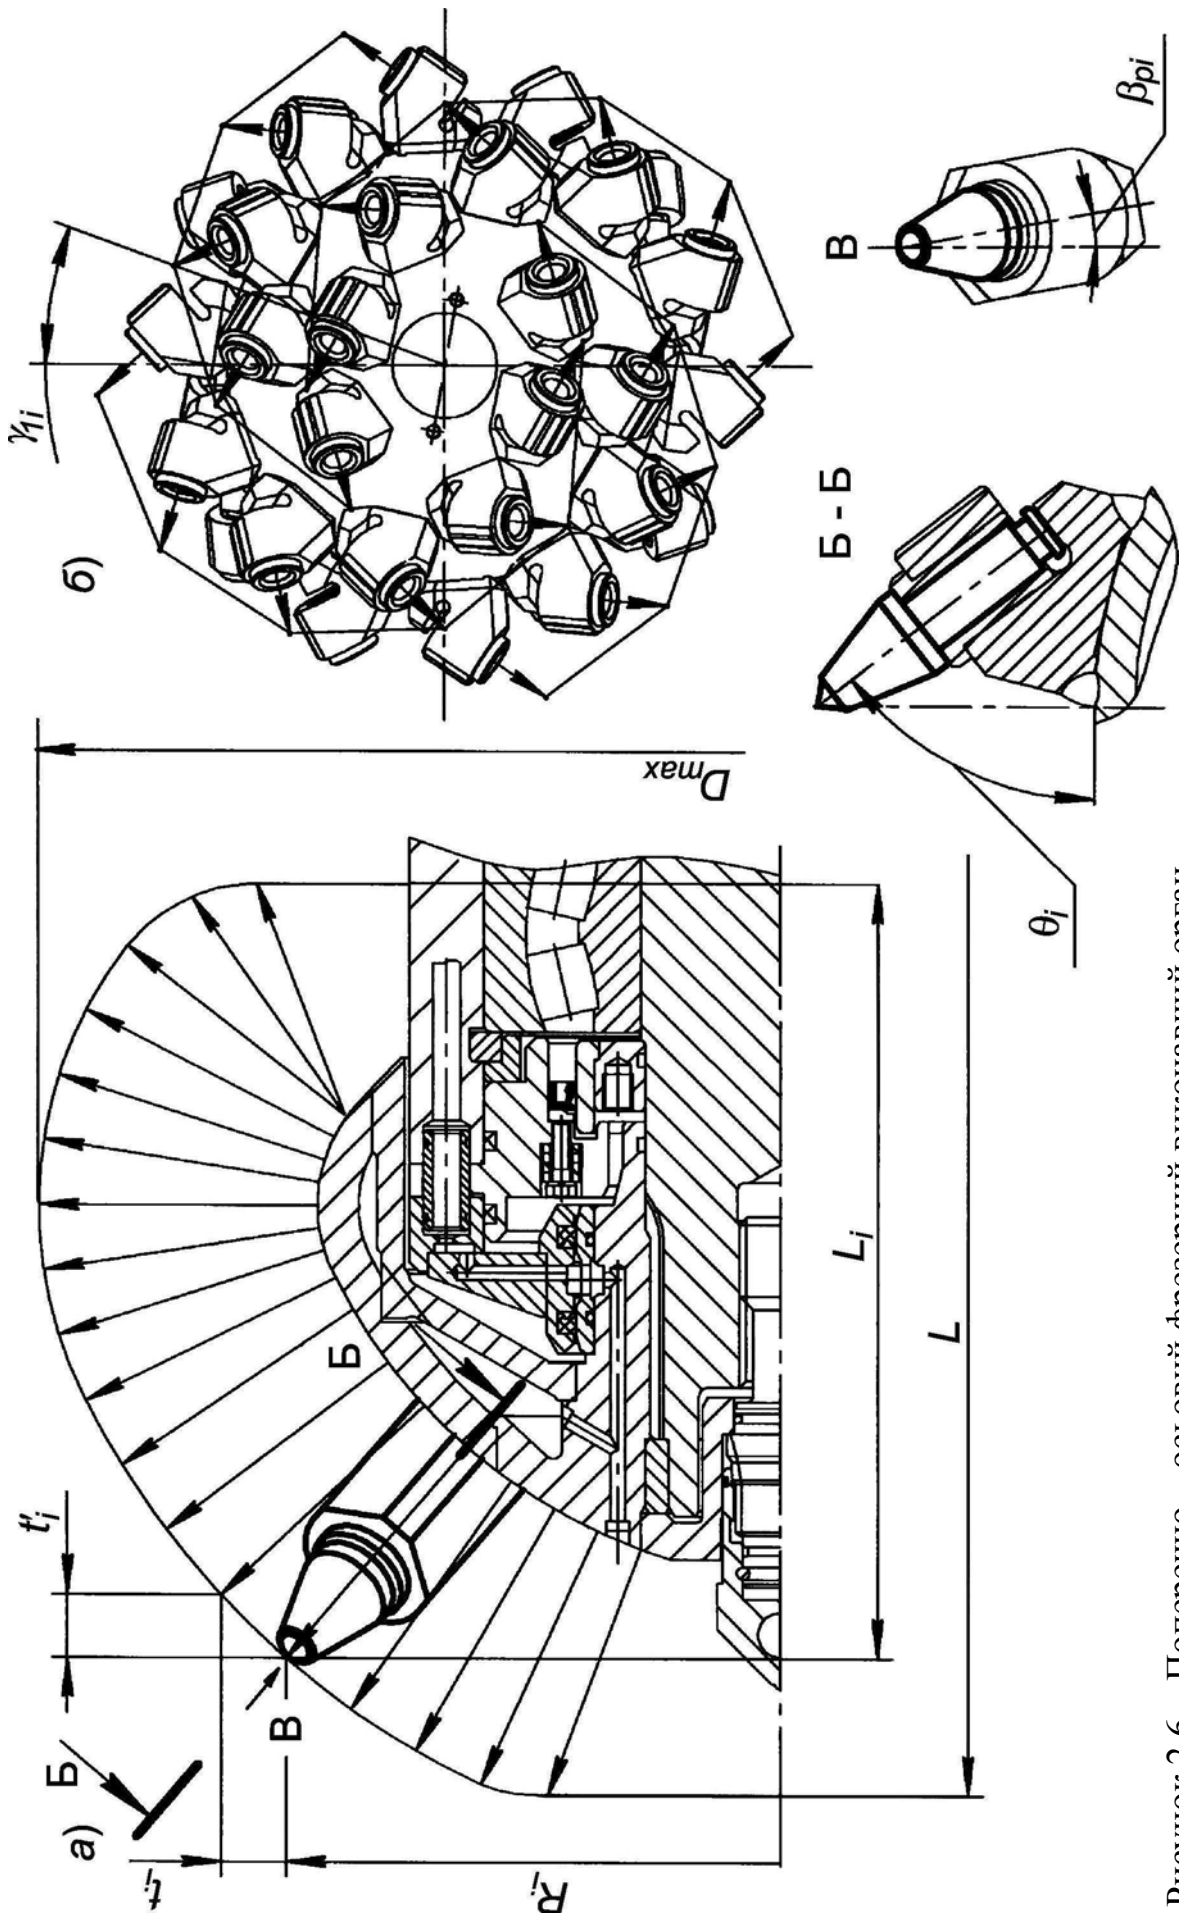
Поперечно – осьовий фрезерний виконавчий орган
